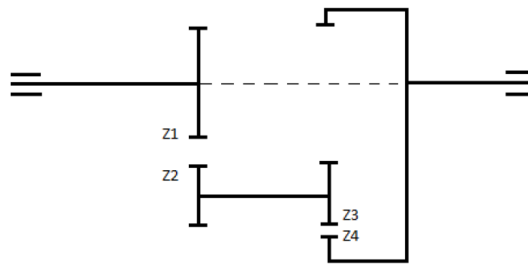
Esquema del sistema de engranajes utilizado en el motor, como se puede observar el engranaje Z1 y el Z4 están conectados entre sí mediante el cigüeñal.
